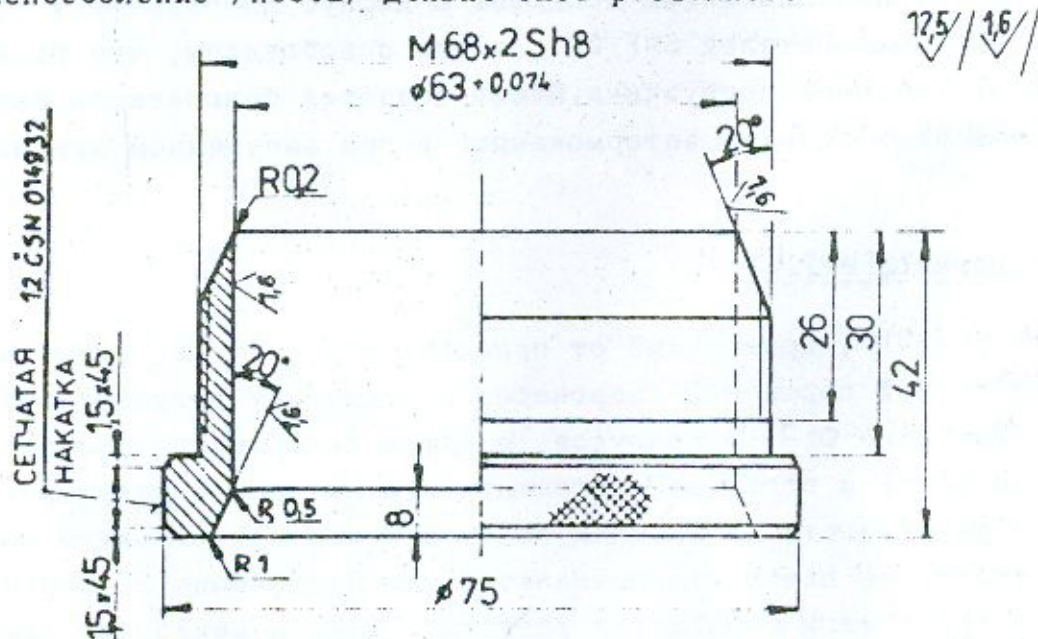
Приспособление для монтажа поршня в прямолинейный гидродвигатель
